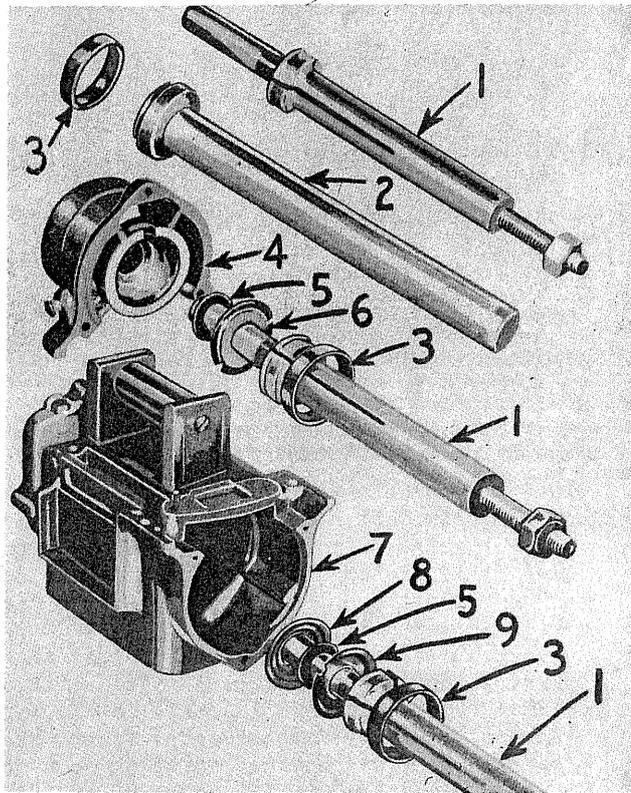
OUTILS UTILISES POUR LE DEMONTAGE ET LE REMONTAGE DES CAGES EXTERIEURES DES ROULEMENTS DE MAGNETOS.
